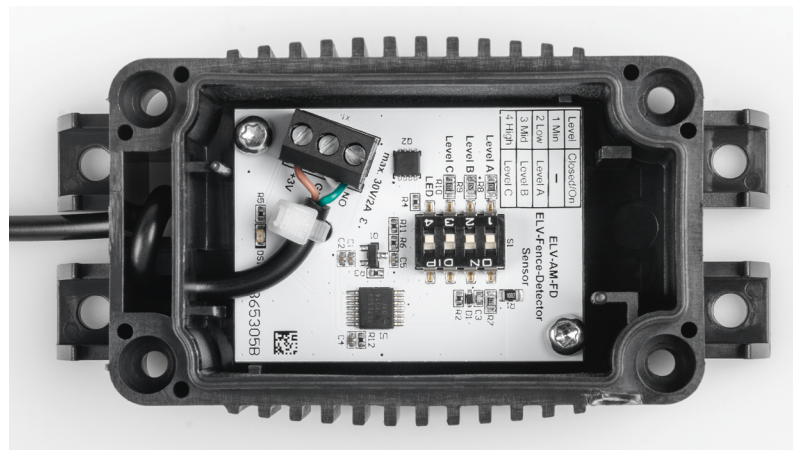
Befestigung der Platine mit den kürzeren Innensechskant-Schrauben
